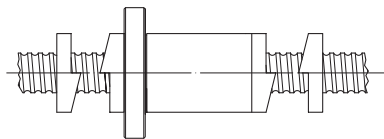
Butée mécanique qui empêche le dépassement du déplacement
